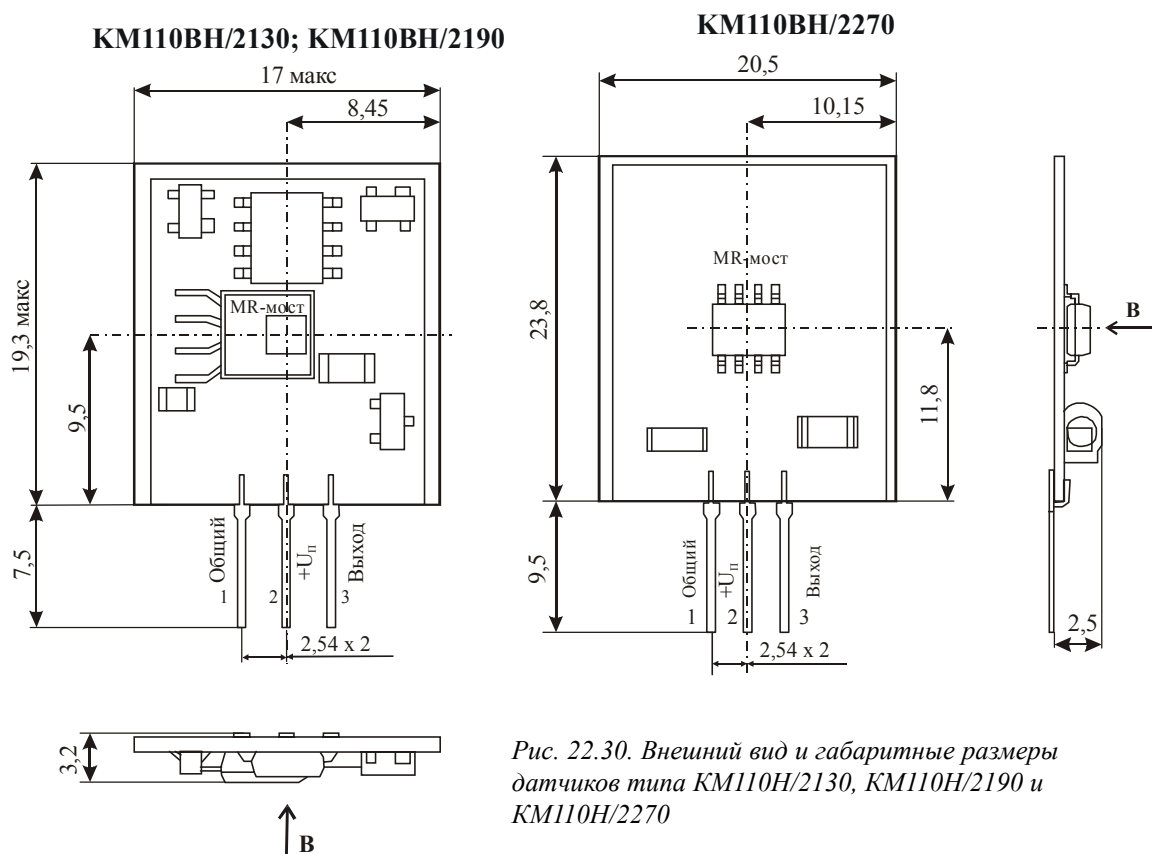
Внешний вид и габаритные размеры датчиков типа KM110H/2130, KM110H/2190 и KM110H/2270
